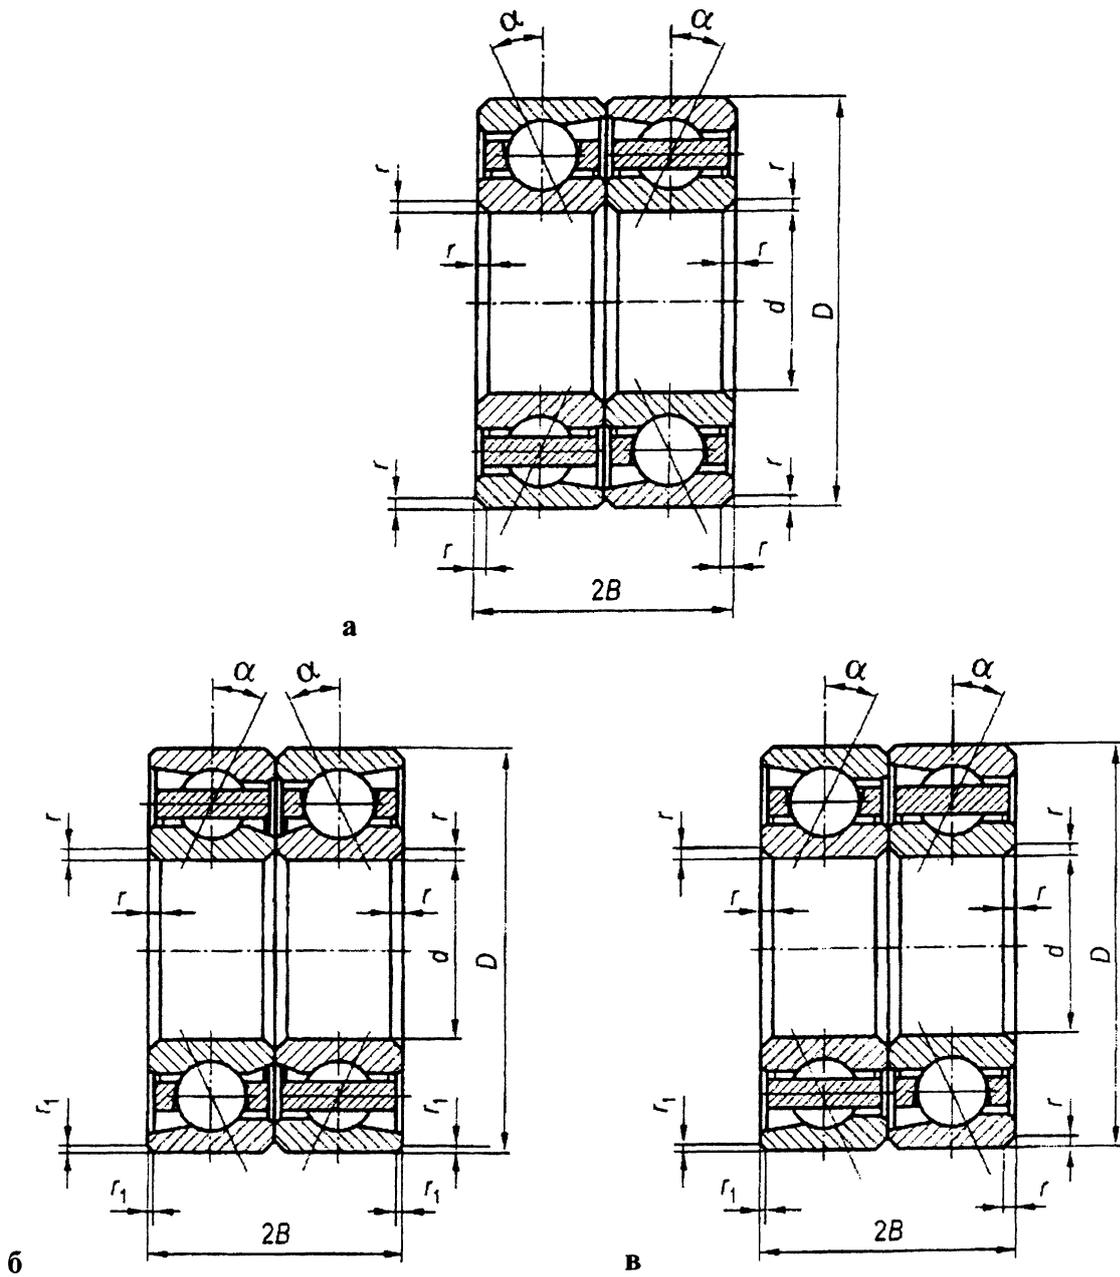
Схемы установки двояных подшипников: а – схема X; б – схема O; в – схема T
